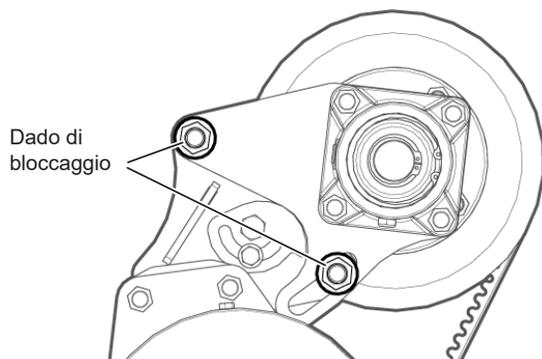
Serrare nuovamente i dadi di bloccaggio
